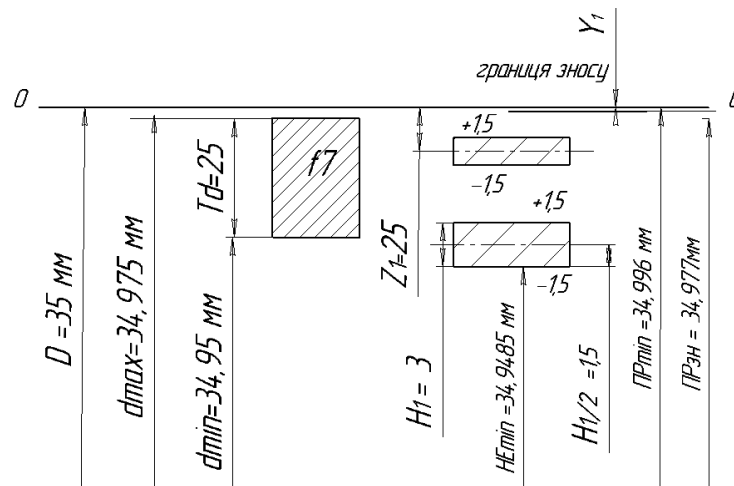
Схема розташування полів допусків для розміру
